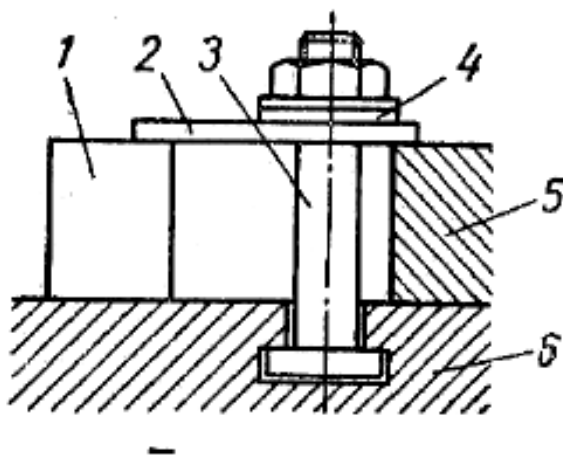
Закріплення заготовки на столі верстата: 1 – підкладка; 2 – прихват; 3 – болт; 4 – шайба; 5 – заготовка; 6 – Т-подібний паз стола
